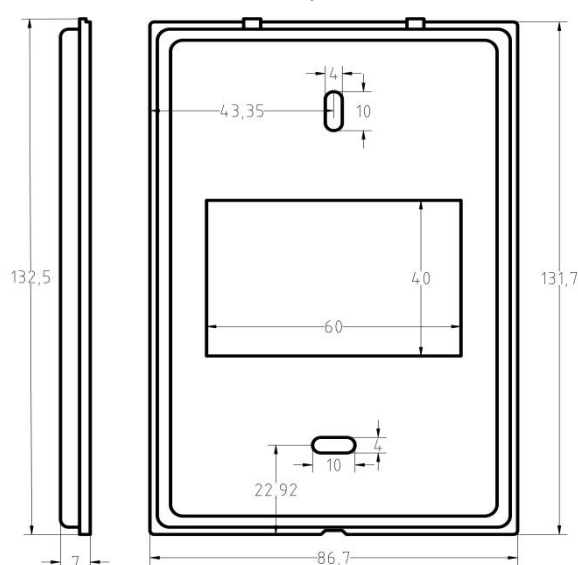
Dimensões da tampa traseira do produto, em milímetros (mm).
